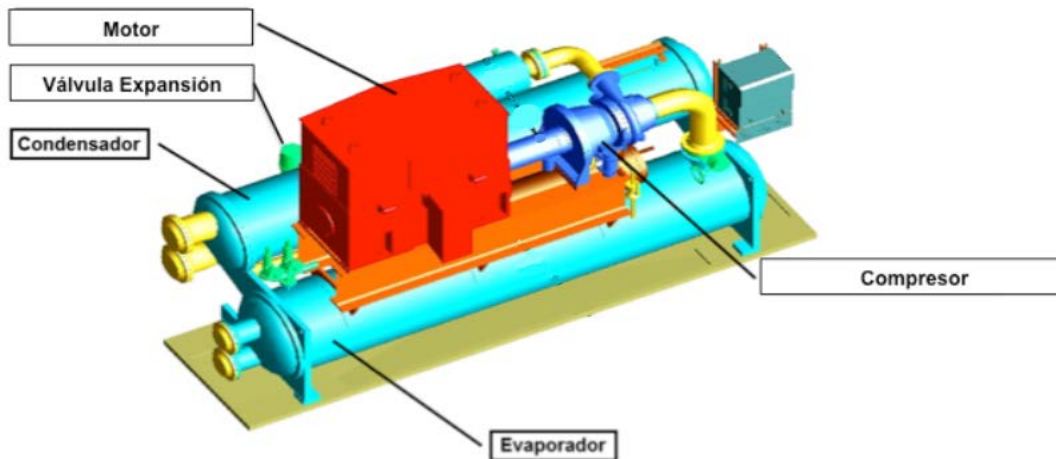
2 : Principales componentes de una bomba de calor industrial
